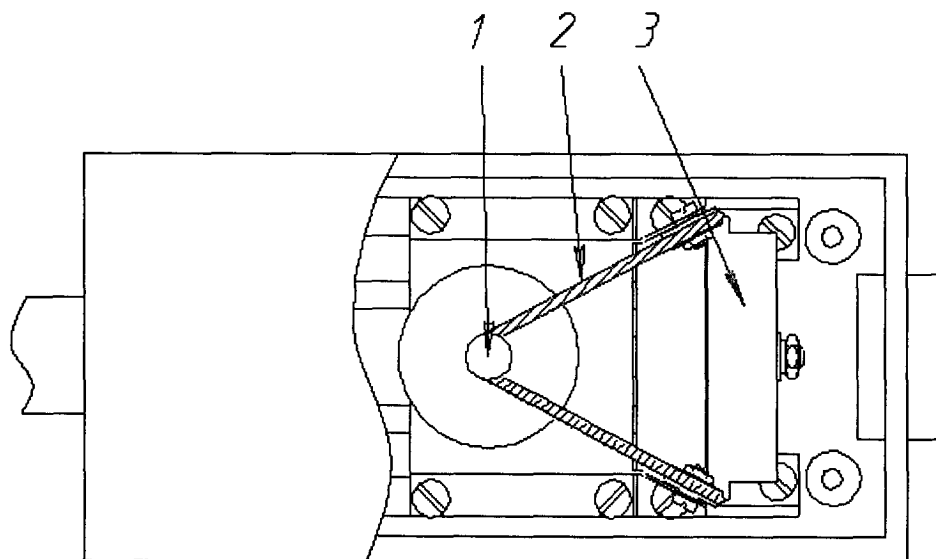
Схематический вид привода сверху при снятой верхней крышке.
